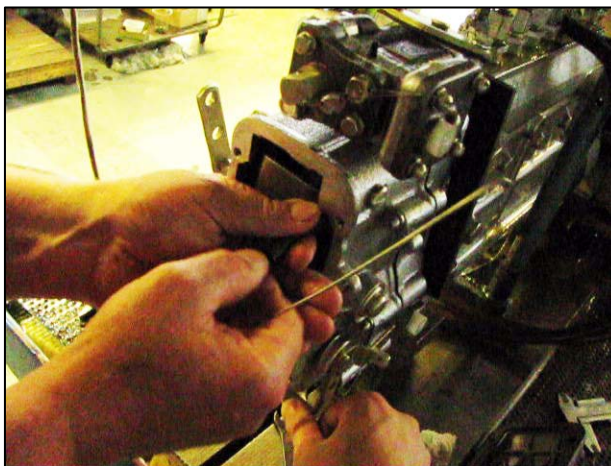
Регулировка начала выключения пусковой подачи
